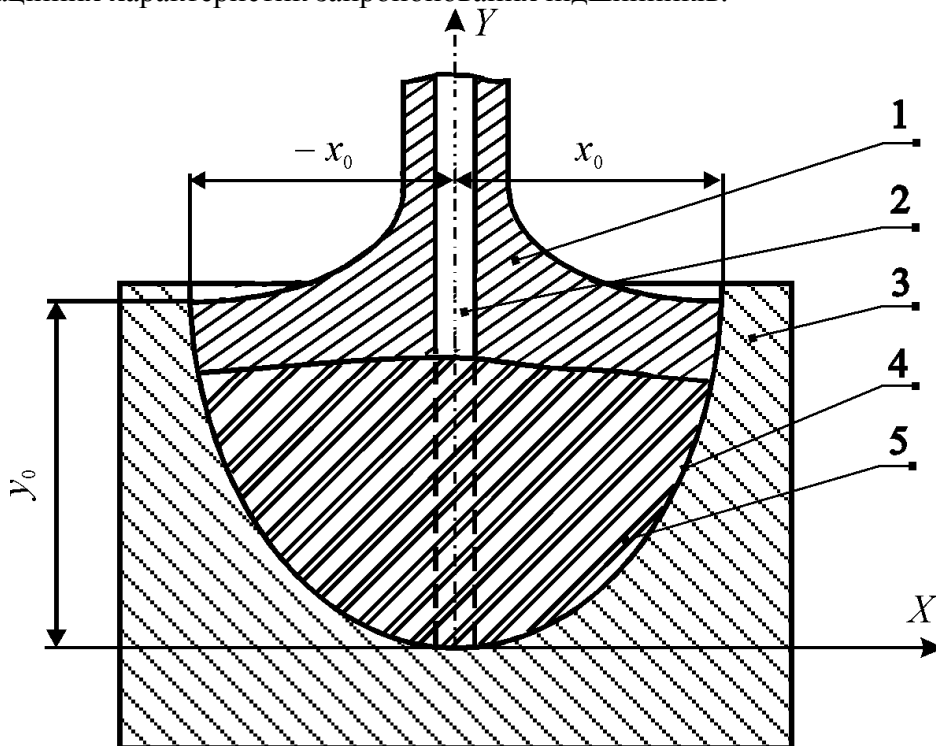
Упорний гідростатичний підшипник з еліпсоїдними робочими поверхнями
